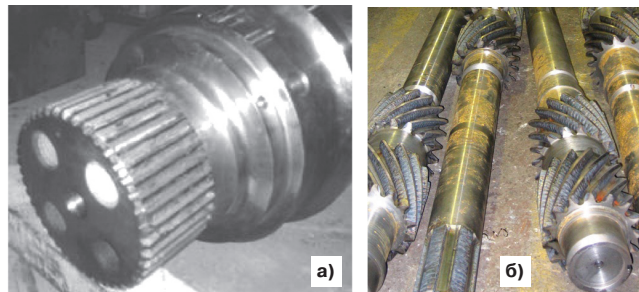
Крупногабаритные детали с плазменной закалкой: а — эджерные валы, б — валы-шестерни.
